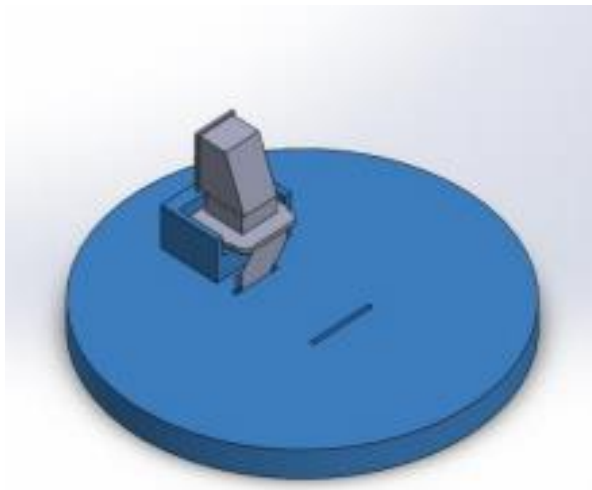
Fixture para operación de soldadura de L Flex, con Detector de Loflo, vista 1.
